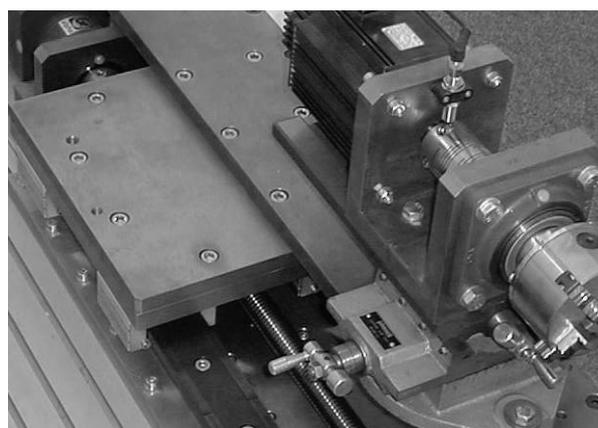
Linearmodul für Entgratungsanlage (Detail), 4 Schlitten GFW-2-48-80 mit Spindeltrieb
